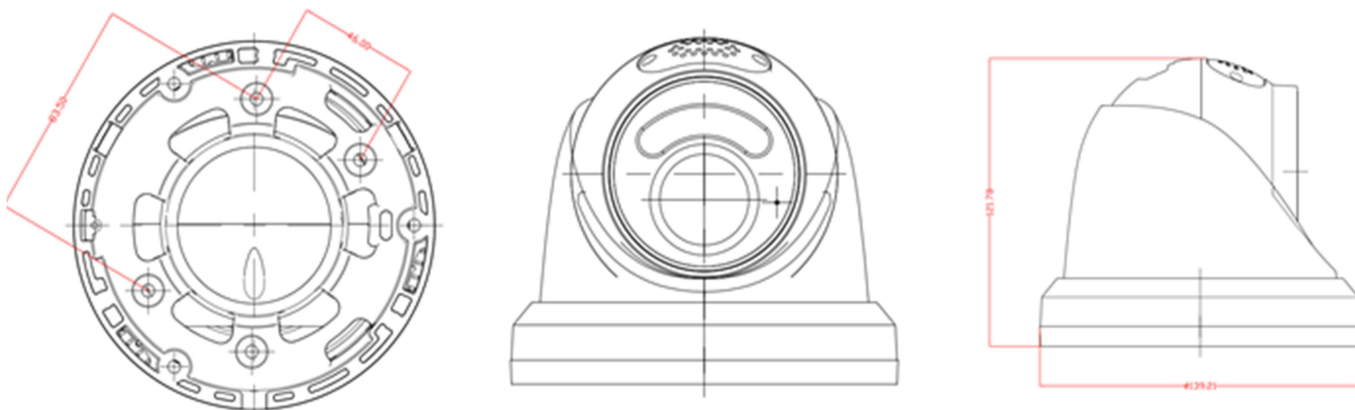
Габаритные и установочные размеры камеры ВД.
